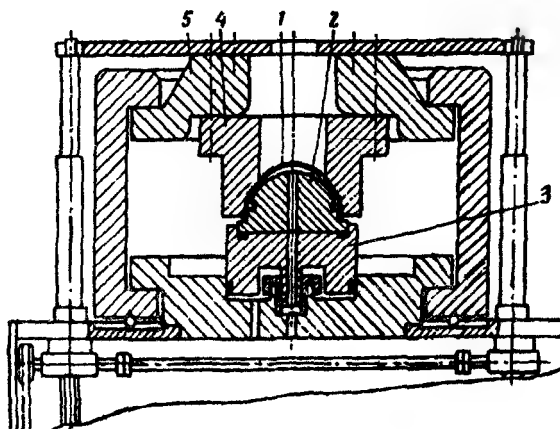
Схема переналадки установки УДР-1 на испытание выпучиванием цилиндрической панели
